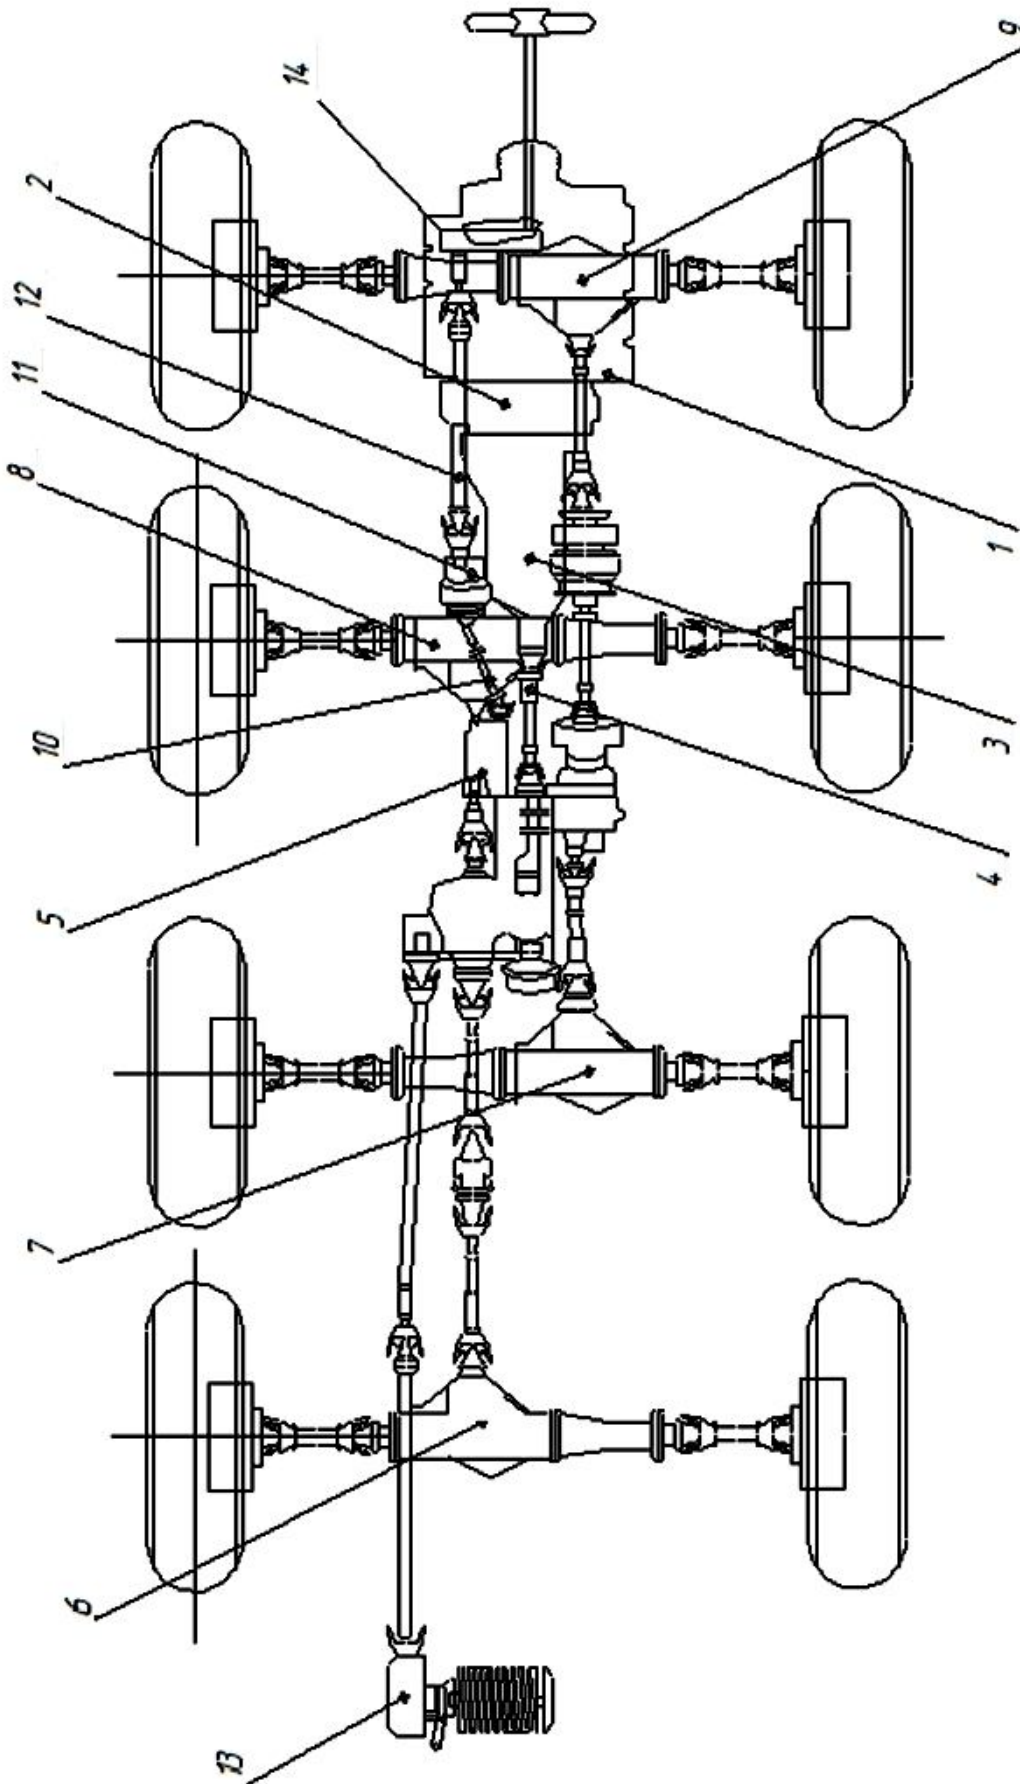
Кінематична схема плаваючої машини: 1 – двигун; 2 – зчеплення; 3 – коробка передач; 4 – проміжний карданный вал; 5 – роздавальна коробка; 6 – перший керований ведучий міст; 7 – другий керований ведучий міст; 8 – третій ведучий міст; 9 – четвертий ведучий міст; 10 – передній карданный вал; 11 – проміжна опора; 12 – задній карданный вал; 13 – редуктор лебідки; 14 – редуктор водомета
